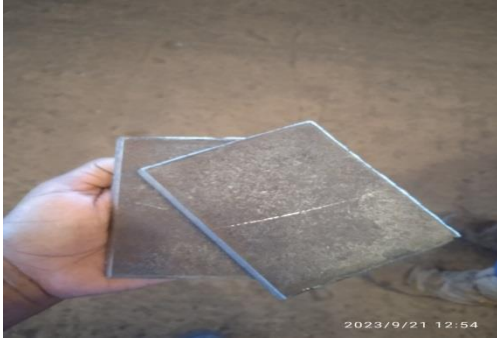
Material base (AISI 1025), sin someterse al proceso de soldadura.
